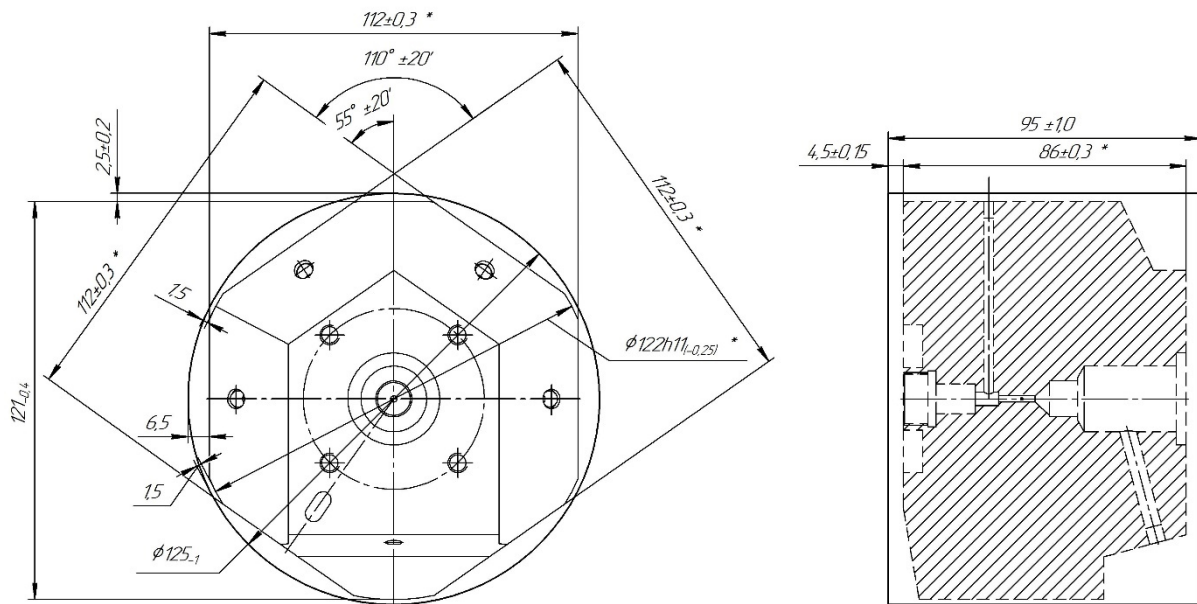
Ескіз заготовки з прокату круглого гарячекатаного
